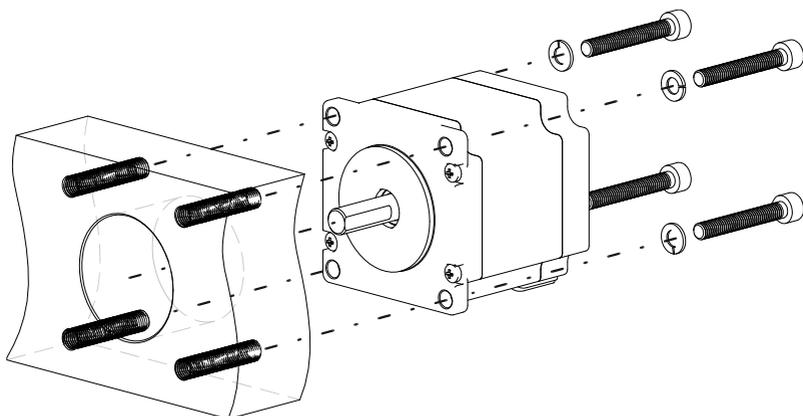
установка двигателей SMO-23, SMO-34 на резьбовые отверстия в плите
